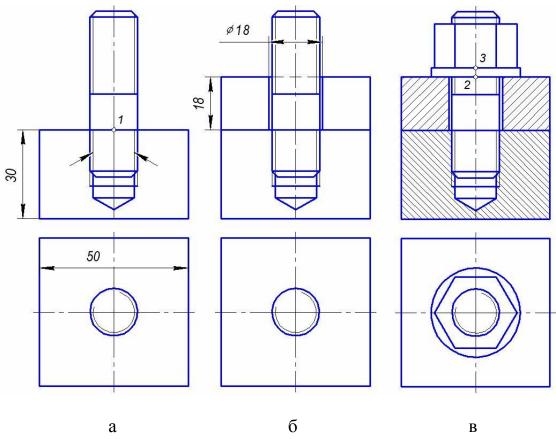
Построение соединения шпилькой: а – вставка шпильки из библиотеки; б – построение изображения присоединяемой детали; в – вставка шайбы и гайки
